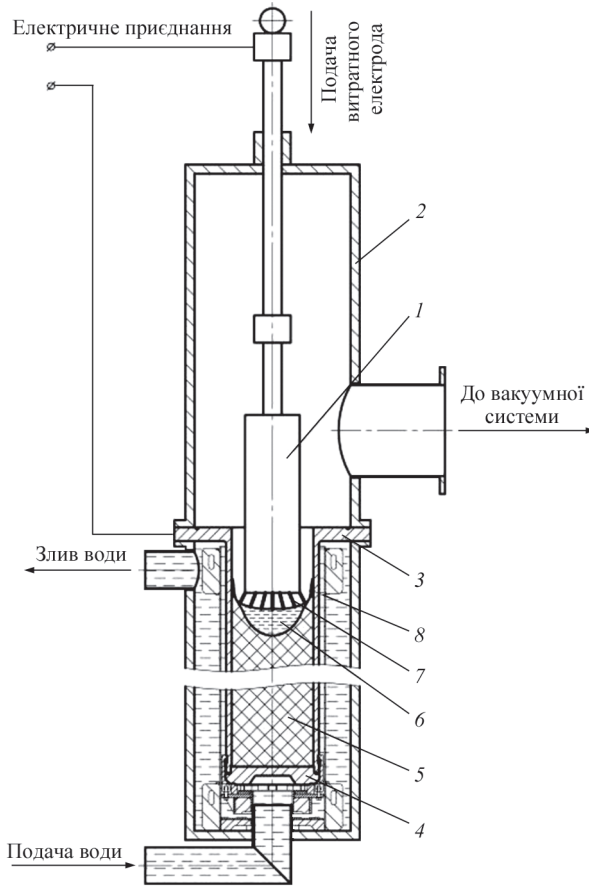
Схема вакуумно-дугової печі з витратним електродом: 1 — піддон; 2 — зливоч; 3 — дуга; 4 — кристалізатор; 5 — витратний електрод; 6 — вакуумна камера; 7 — «корона», головна частина зливка
